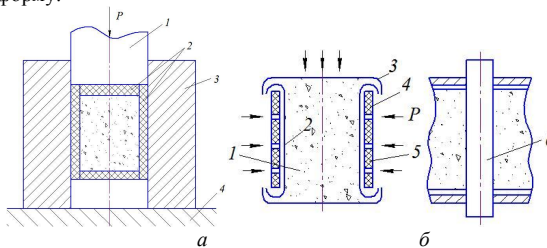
Схема изостатического прессования: 1 – пуансон пресса; 2 – эластичная оболочка; 3 – металлическая пресс-форма; 4 – стол пресса
